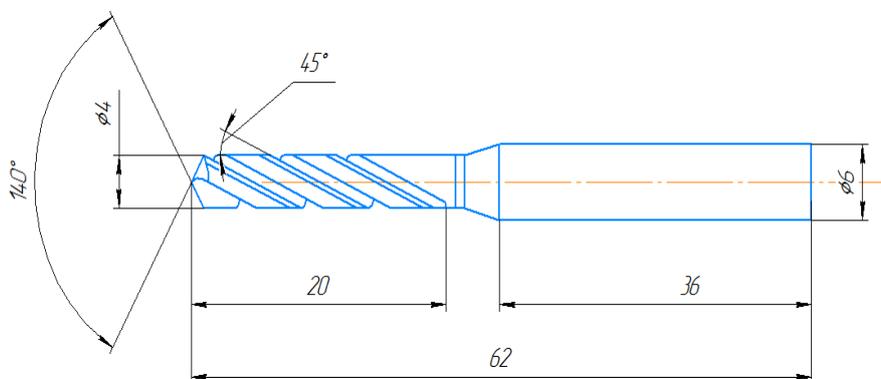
Эскиз режущего инструмента – сверла фирмы Iscar
